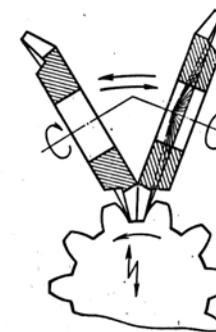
Схема нарезания зубьев зубчатых колес методом обкатки с использованием двух дисковых фрез
